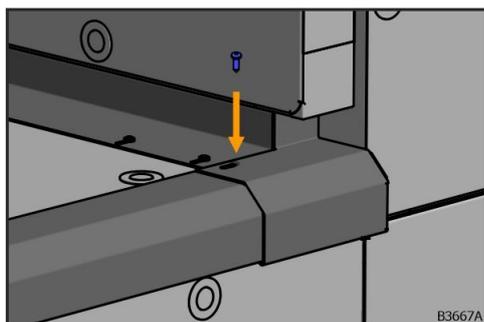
Montage de l'extrémité de la cornière casse-goutte
